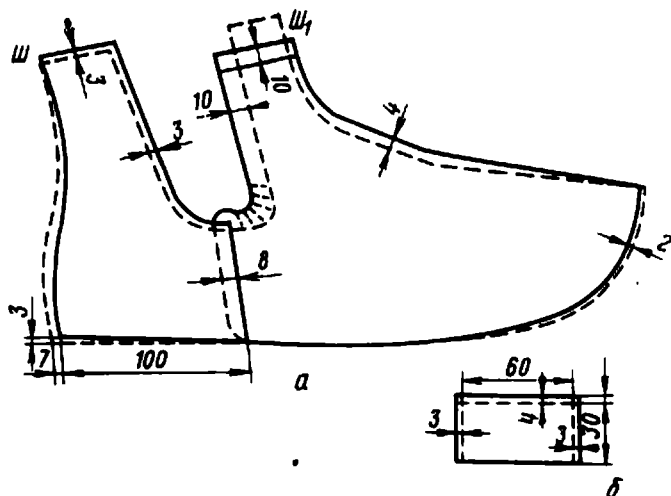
Модель подкладки мужского ботинка с резинками и отрезными деталями:
